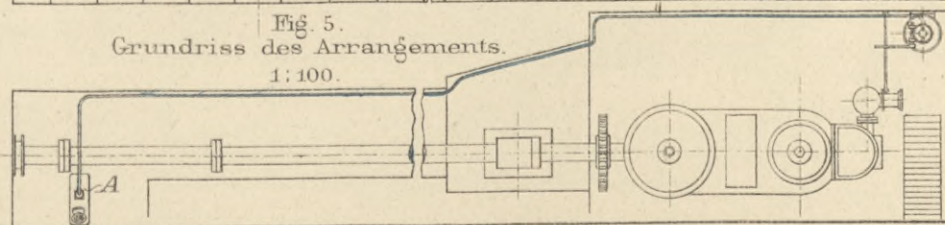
Grundriss des Arrangements. 1:100.
